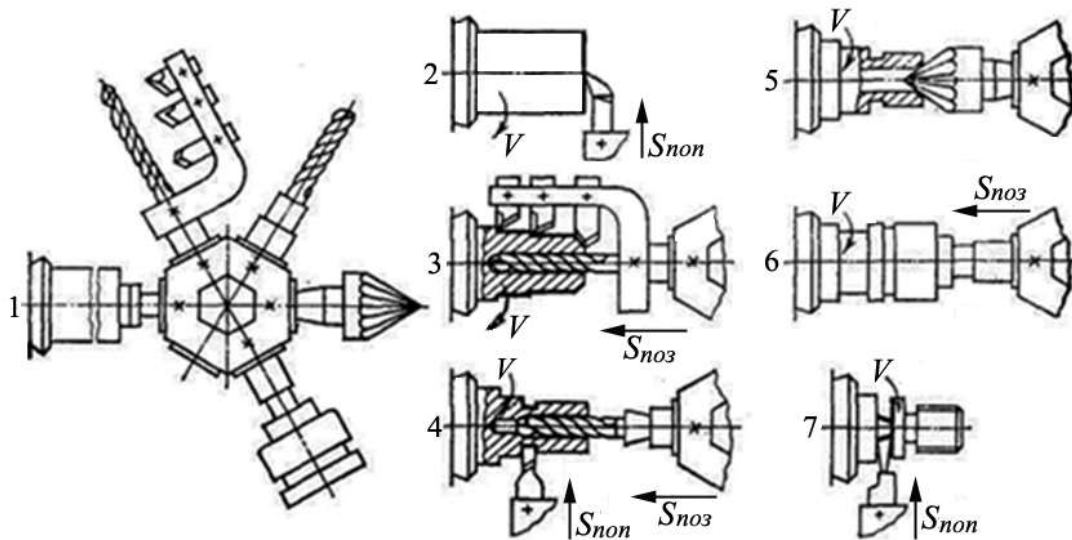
Схема налагодження токарно-револьверного верстата для обробки різьбової пробки:
